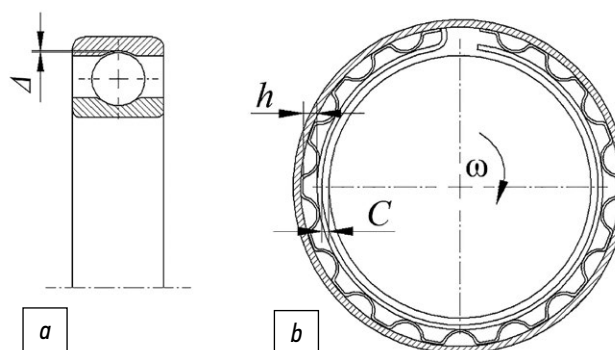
Источники зазоров в шариковом подшипнике качения (a) и лепестковом газодинамическом подшипнике (b): Δ – радиальный зазор; C – монтажный зазор, h – высота гофров упругого демпфера.
